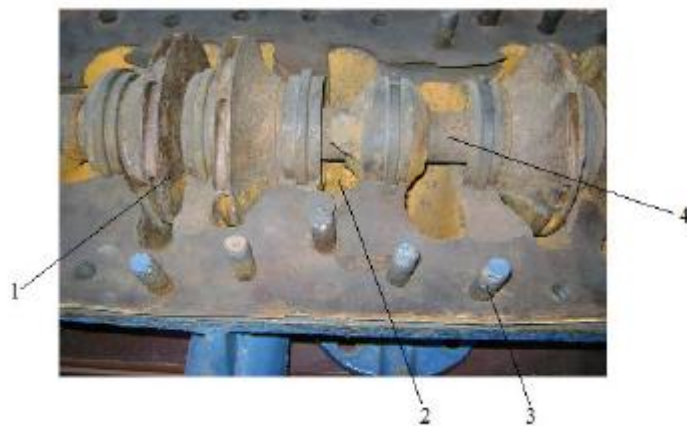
Абразивний знос відцентрового насоса: 1 – знос робочого колеса; 2 – знос внутрішньої поверхні корпусу; 3 – знос шпильок; 4 – корозія поверхні валу.
